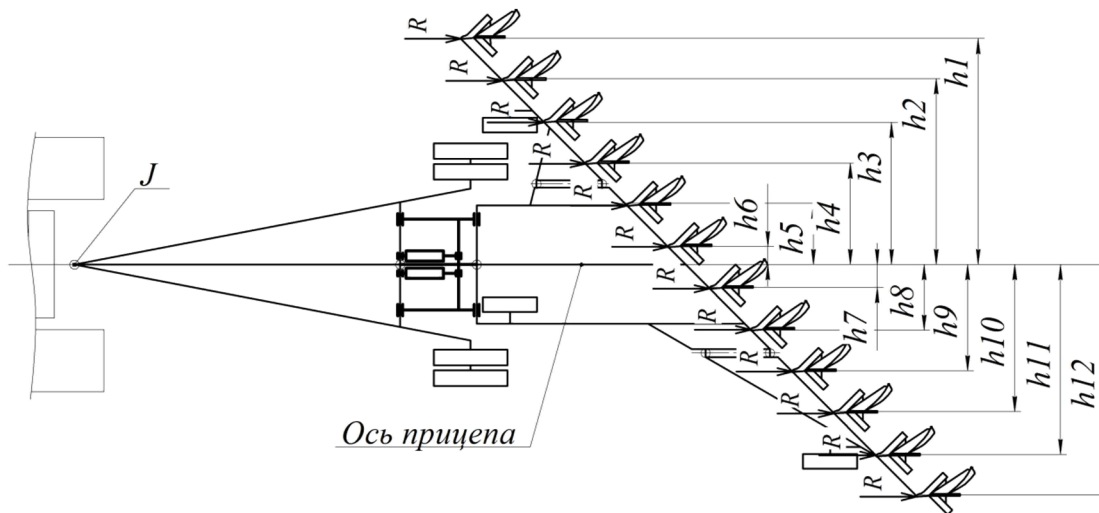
Схема уравнивания 12-корпусного прицепного плуга
